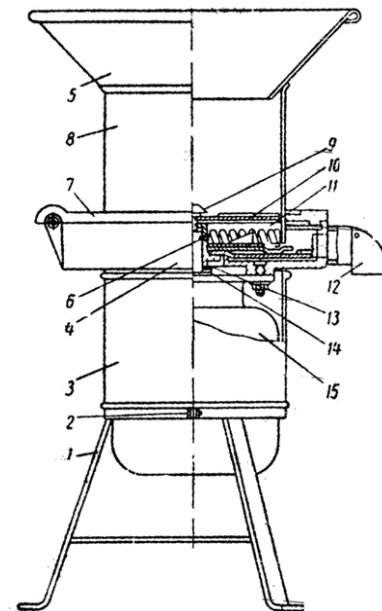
Коренерізка КП-4: 1-рама; 2-стяжний болт; 3-кожух; 4-корпус камери подрібнення; 5-завантажувальна горловина; 6-штифт; 7-кришка камери подрібнення; 8-бункер; 9-спеціальний болт; 10-верхній диск; 11-дека з зубами ; 12-вивантажувальний рукав; 13-гумовий сальник; 14-регулювальні кільця; 15-електродвигун.
